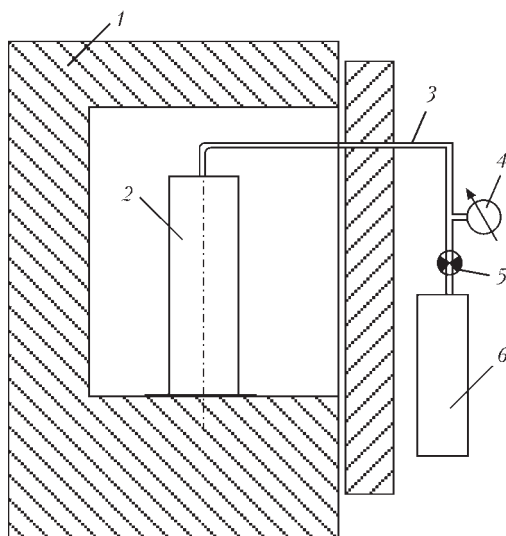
Схема проведения автономной вакуумной напайки: 1 — термическая печь; 2 — опытная заготовка; 3 — вакуумпровод; 4 — мановакуумметр; 5 — вентиль; 6 — форвакуумный насос
